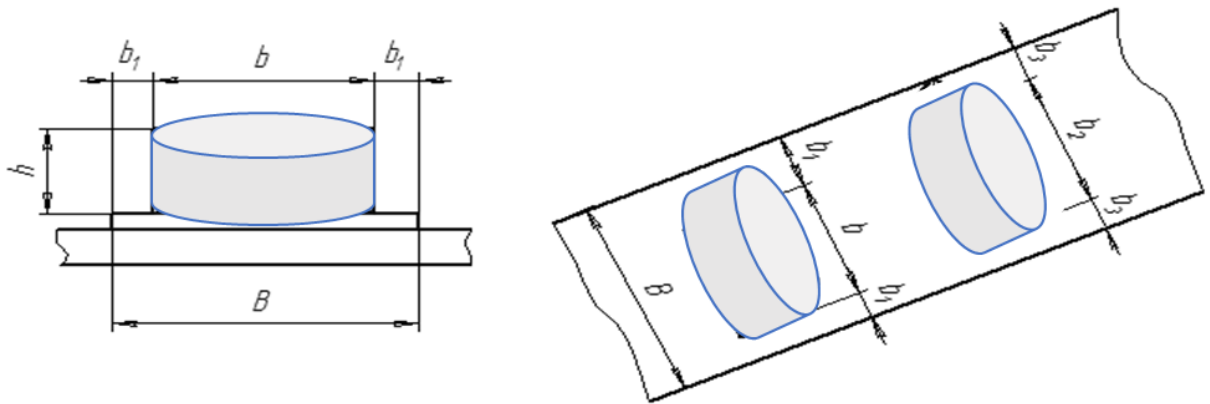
Схема для розташування об'єкту обробки на поверхні - стрічки конвеєра
